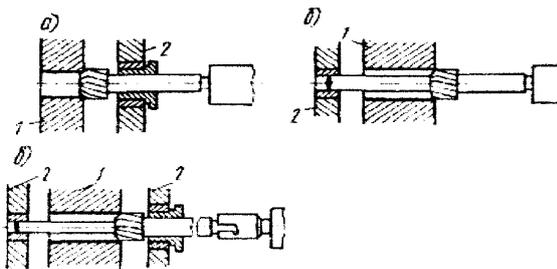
Схемы направления инструмента при растачивании отверстий в корпусных деталях:
